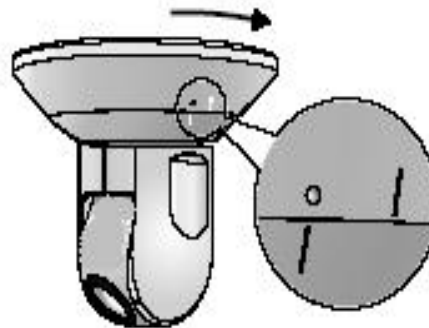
Ajuste de la cubierta de instalación en el techo con la cámara
